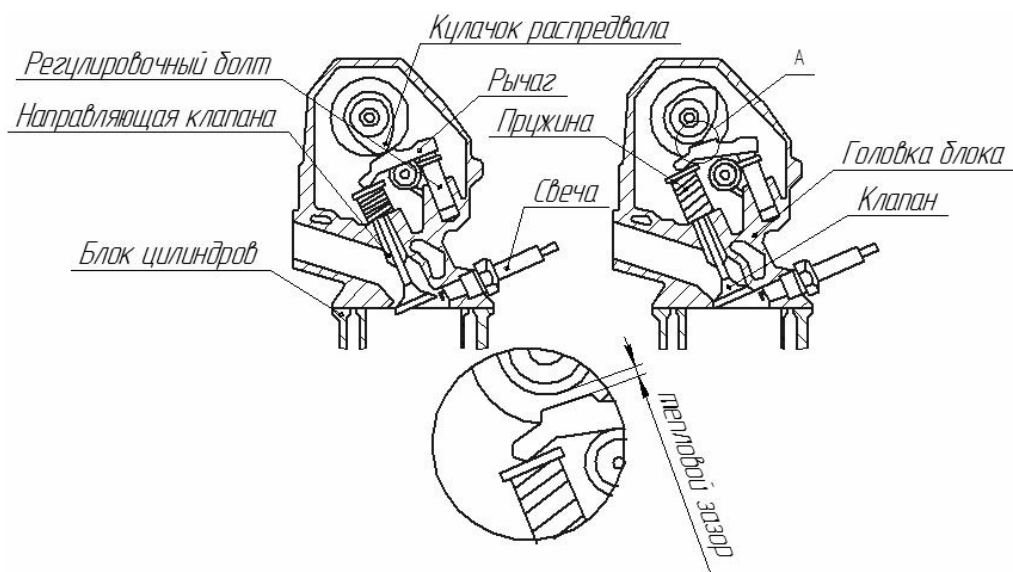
Схема работы газораспределительного механизма двигателя с верхним расположением распределительного вала
